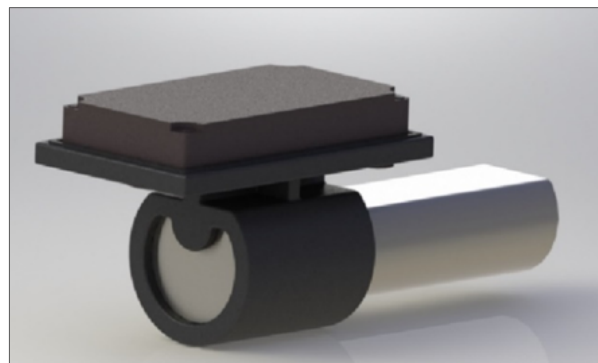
Linearmagnet mit Halter, Befestigung auf einer Achse
